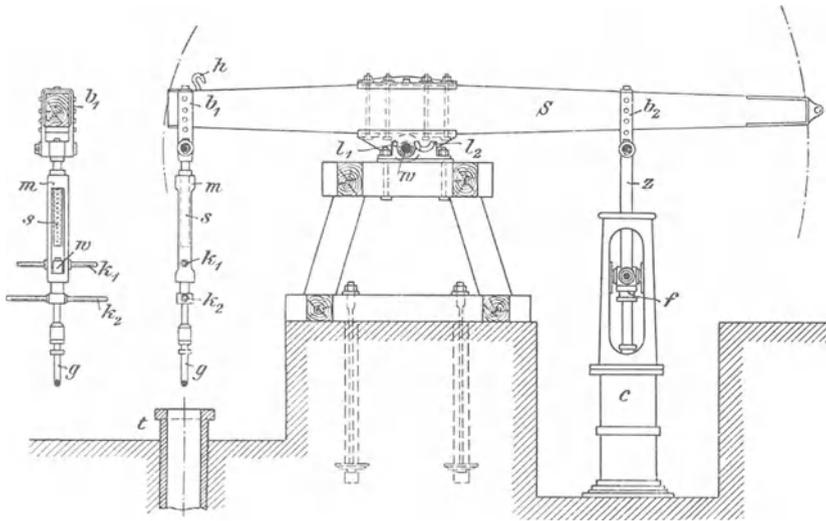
Bohrschwengel mit Schlagzylinder und Bohrtäucher.
